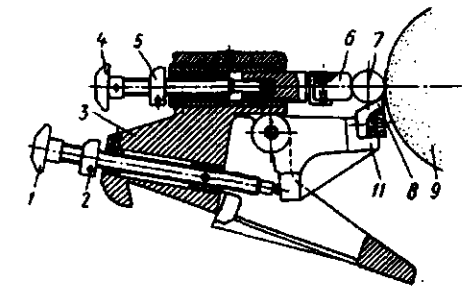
Двухопорный люнет: 1 и 4 — винты; 2 и 5 — упорные кольца; 3 — корпус люнета; 6 и 8 — опорные колодки; 7 — обрабатываемая деталь; 9 — шлифовальный круг
